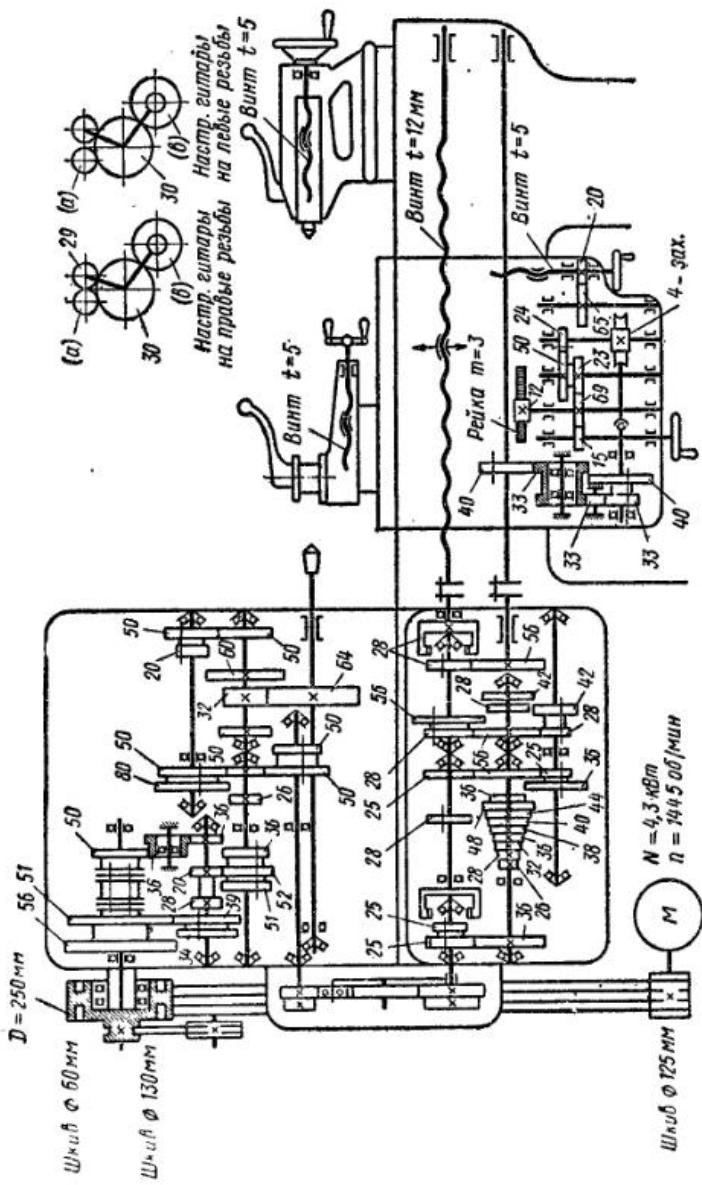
Кинематическая схема станка 1Д62 (цифрами обозначены числа зубьев)
